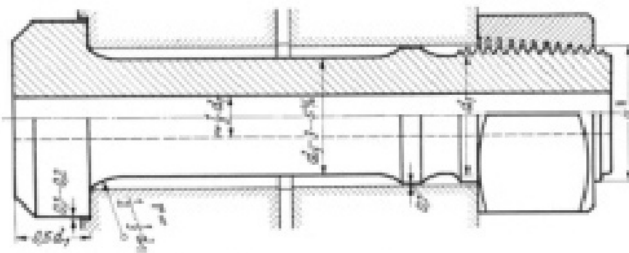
Vierflügelige Flenschraube nach SOLT für 50 t Tragkraft.
